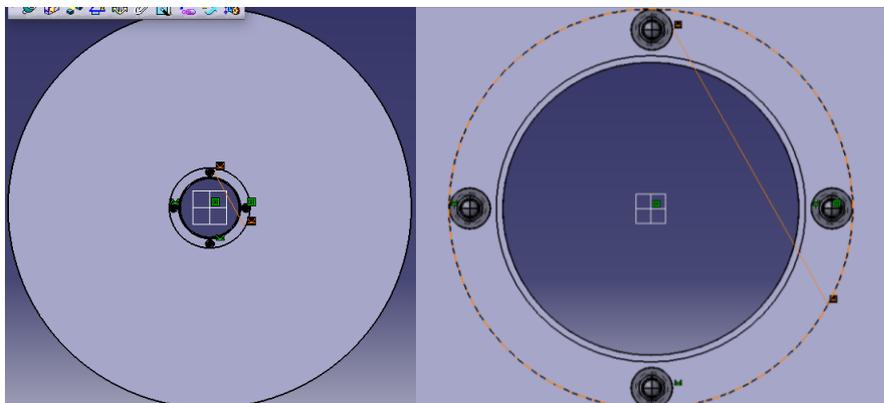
Zona de colocación de los rodamientos, planta.
